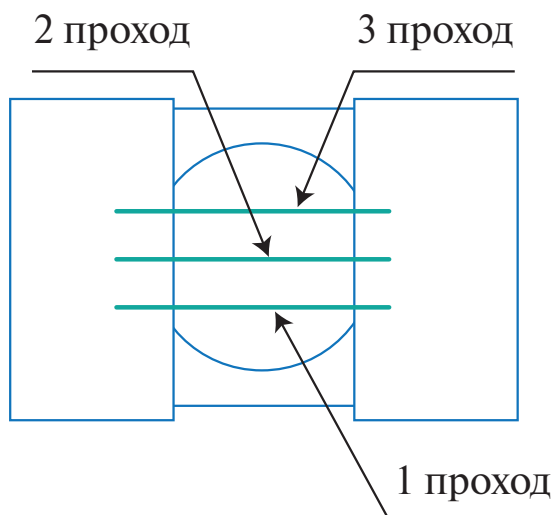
Схематический чертеж расположения проходов при наплавлении
